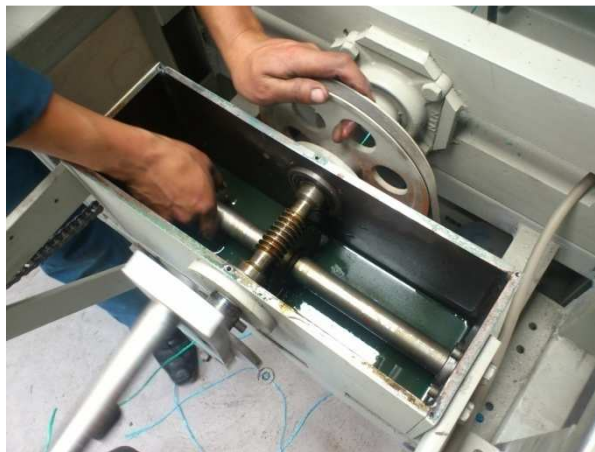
Montaje Engranaje Tornillo sin Fin
